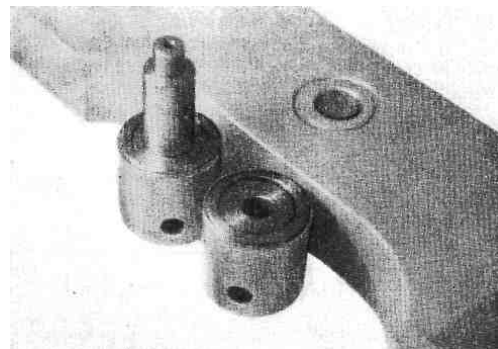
Образец с цилиндрическим отверстием и обжимки (пуансоны) для формообразования концентрических кольцевых канавок вокруг отверстия
